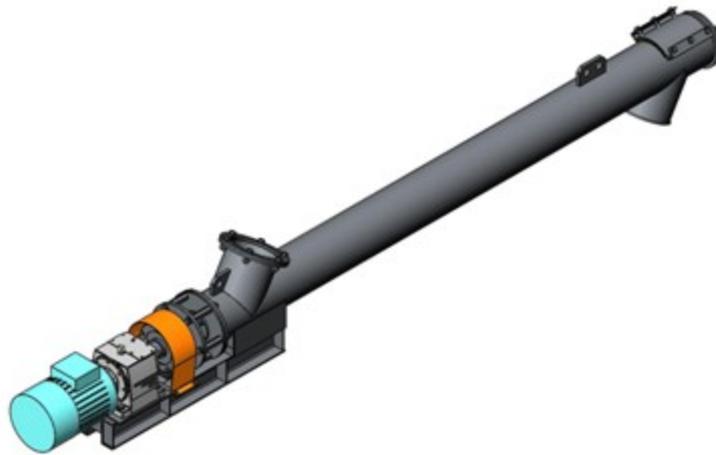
Пример конструкций трубчатого шнекового транспортера
